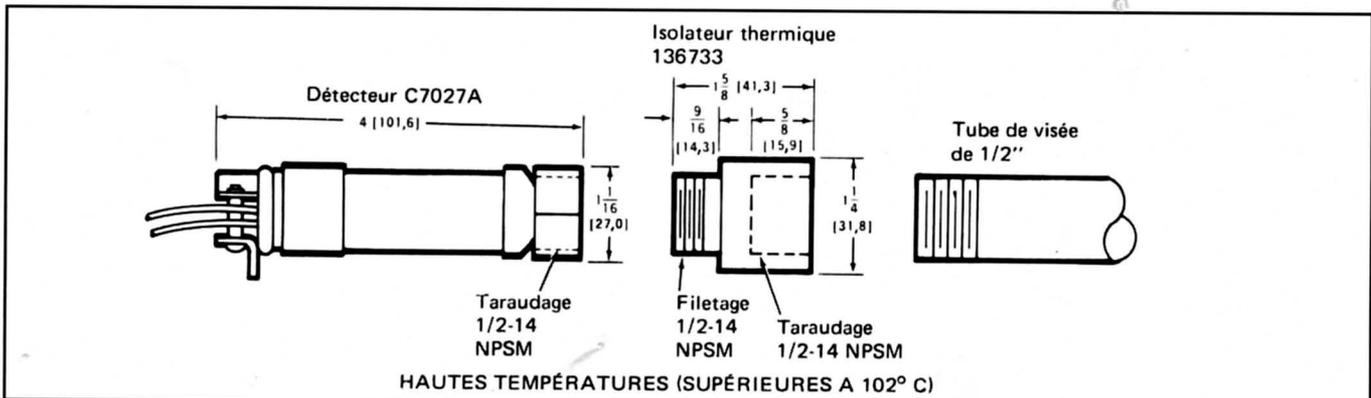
Dimensions de montage de l'isolateur thermique 136733
